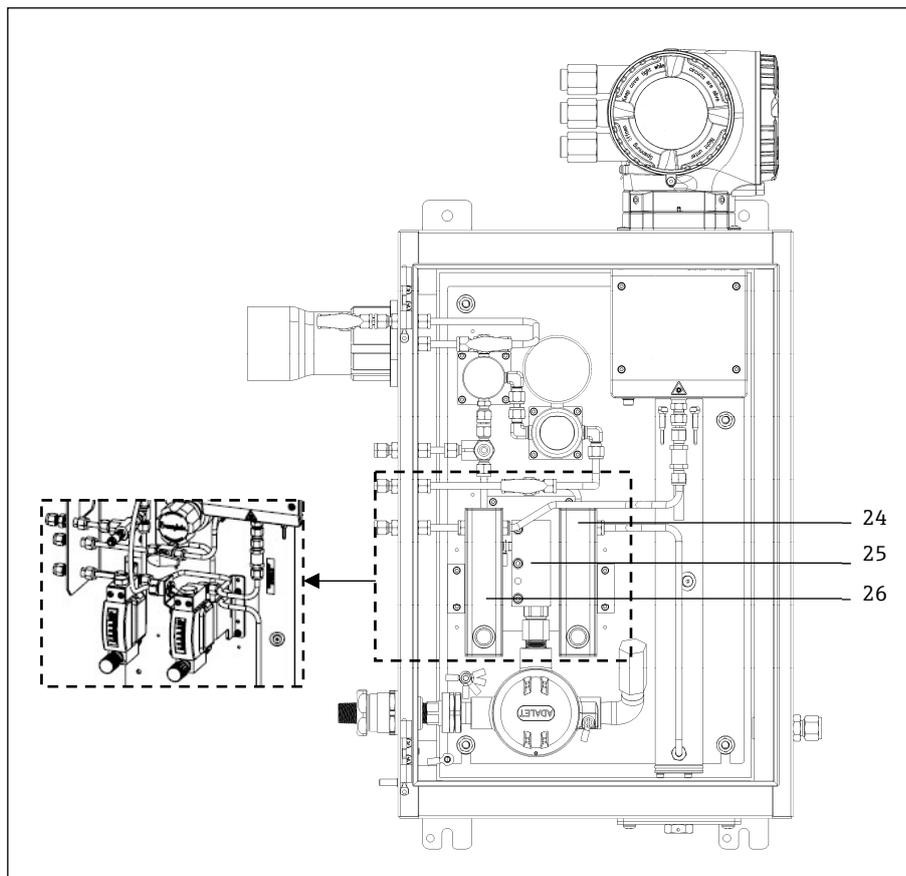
Запасные части для анализатора J22 с системой подготовки проб в корпусе
